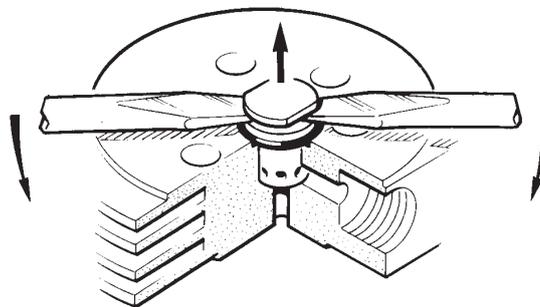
Напорный клапан 3-й ступени, демонтаж
